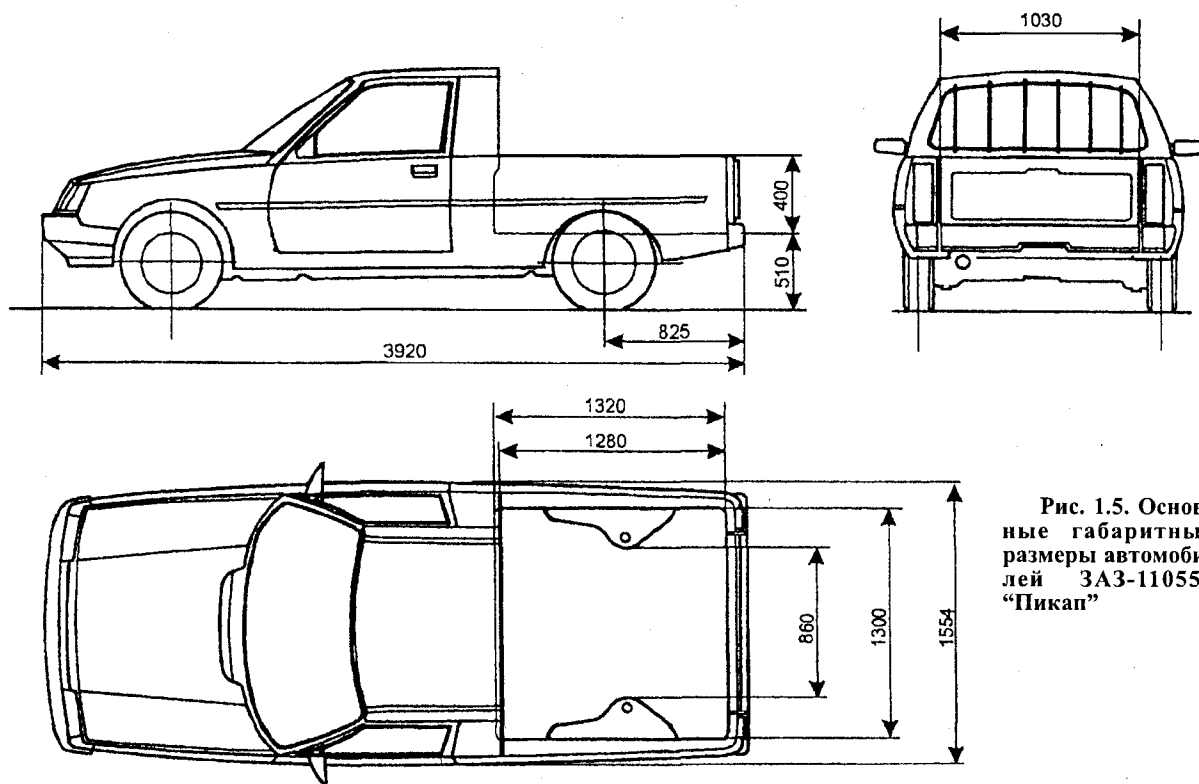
Основные габаритные размеры автомобилей ЗАЗ-110550 «Пикап»
